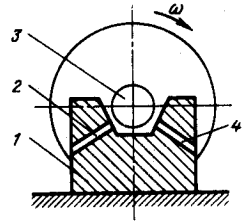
Схема стенда для статической балансировки роторов с шарикоподшипниковыми опорами и наложением вибрации: 1 — электромагнит; 2 — якорь; 3 — опоры стенда с шарикоподшипниками; 4 — ротор
